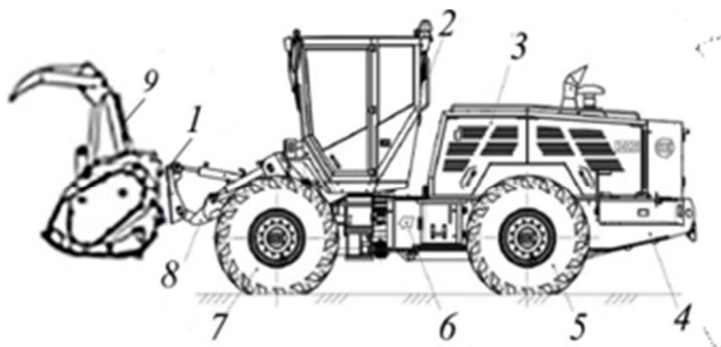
Общий вид мульчера: 1 – адаптер; 2 – кабина; 3 – установка силовая; 4 – рама; 5, 7 – ведущие мосты с колесами; 6 – коробка раздаточная; 8 – стрела.
